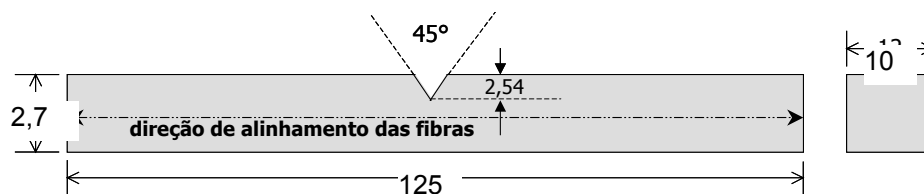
Esquema do corpo de prova padrão para ensaio de impacto Charpy (dimensões em mm).
